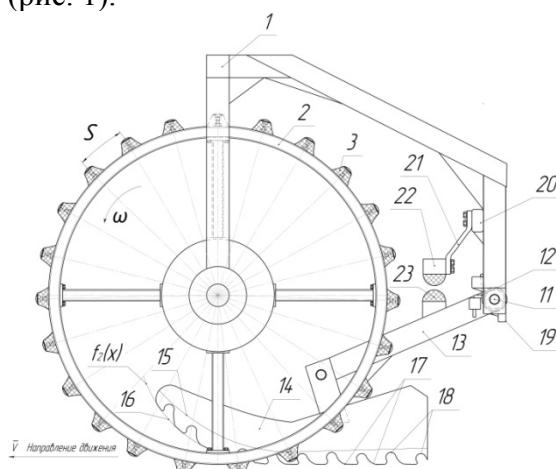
Вид сбоку тандемного почвообрабатывающего катка
